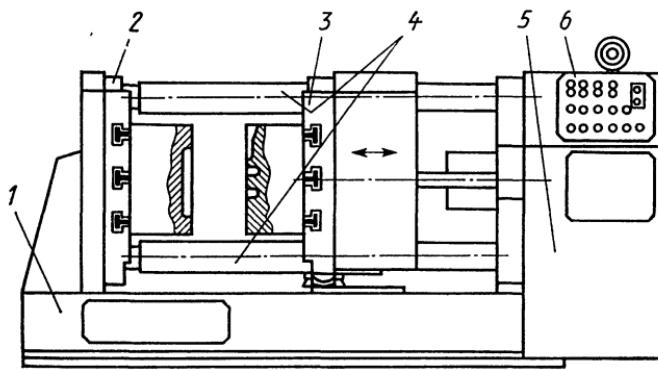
Кокильная машина для изготовления отливок простой формы
